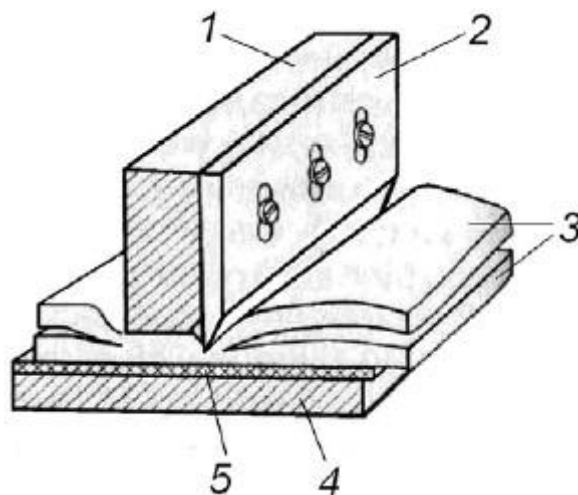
Форма электрода для сварки с одновременным обрезанием: 1 – электрод; 2 – обрезной нож; 3 - свариваемые пленки; 4 - низкопотенциальный электрод; 5 – диэлектрическая прокладка
